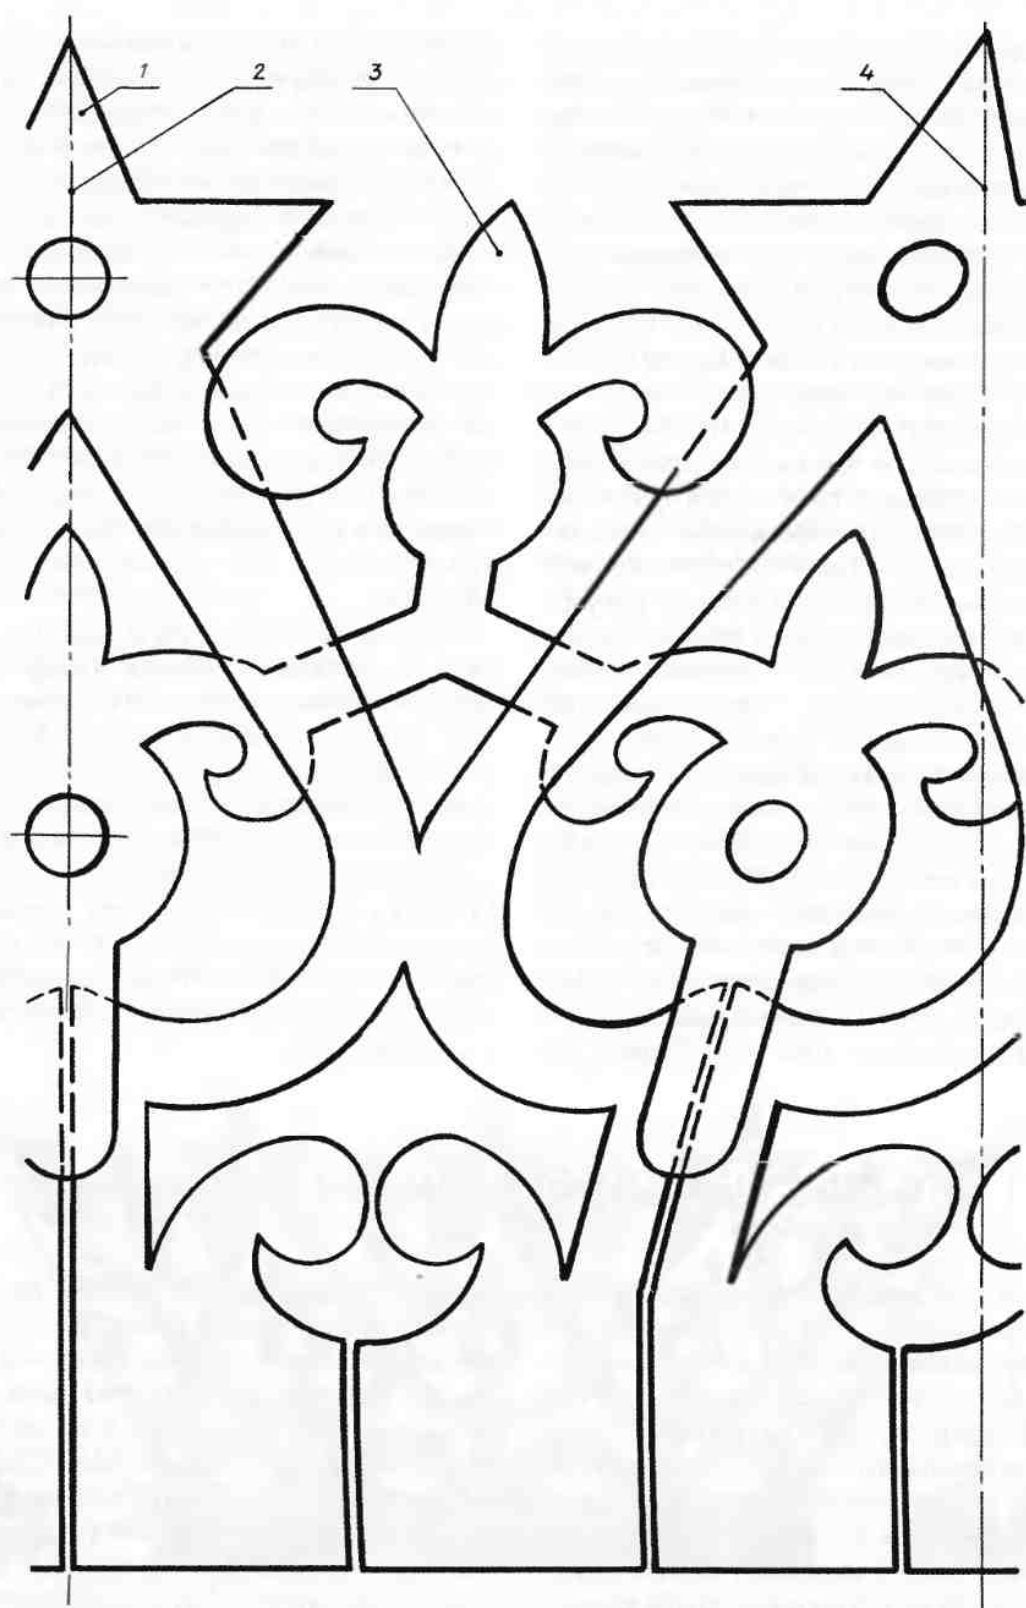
Выкройка средней части трубы: 1 — основная деталь; 2 — средняя линия чертежа; 3 — дополнительные детали; 4 — линия стыка выкройки угловой детали
